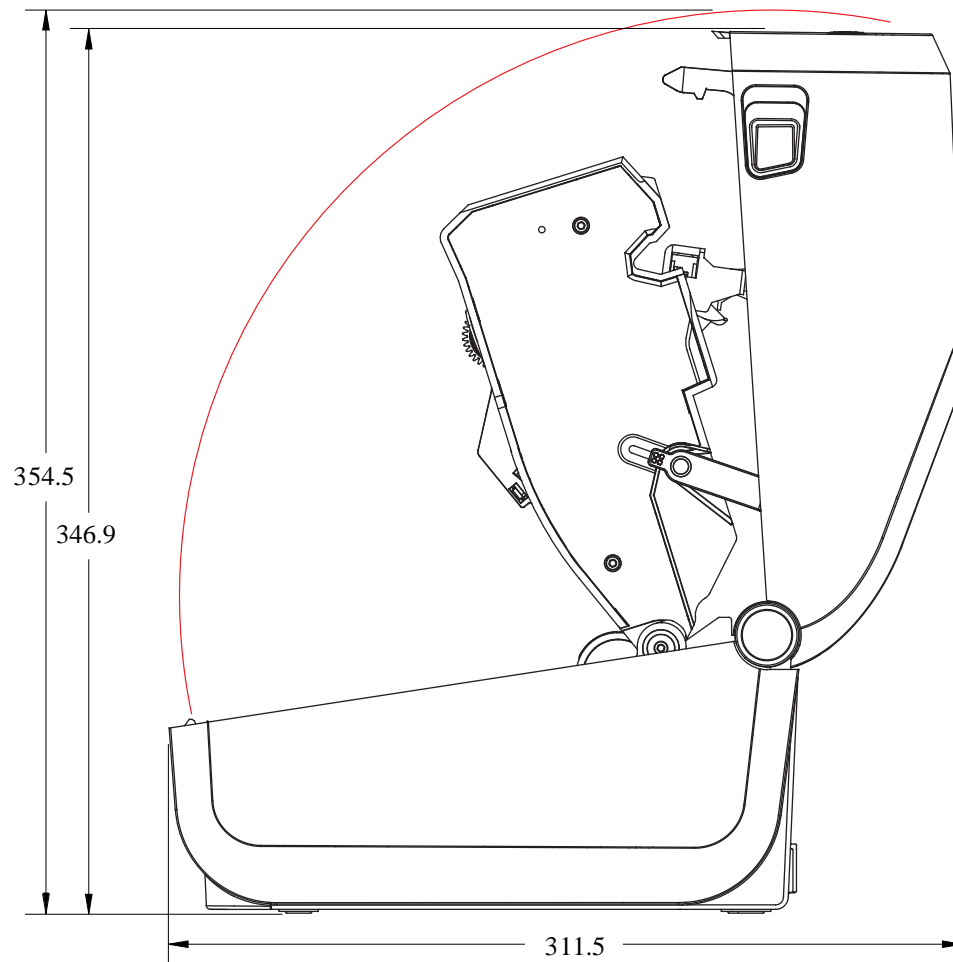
Modelos de impressora ZD421C (Transferência térmica do cartucho de fita) – dimensões da impressora padrão
